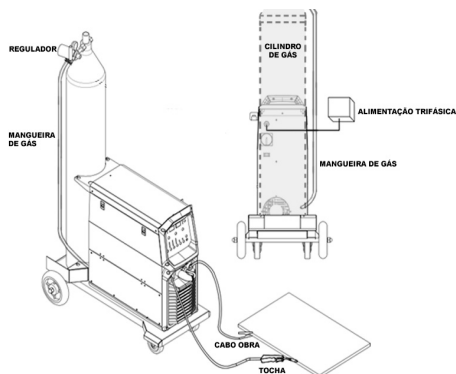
Montagem dos cabos de solda no modo MIG/MAG com gás de proteção
